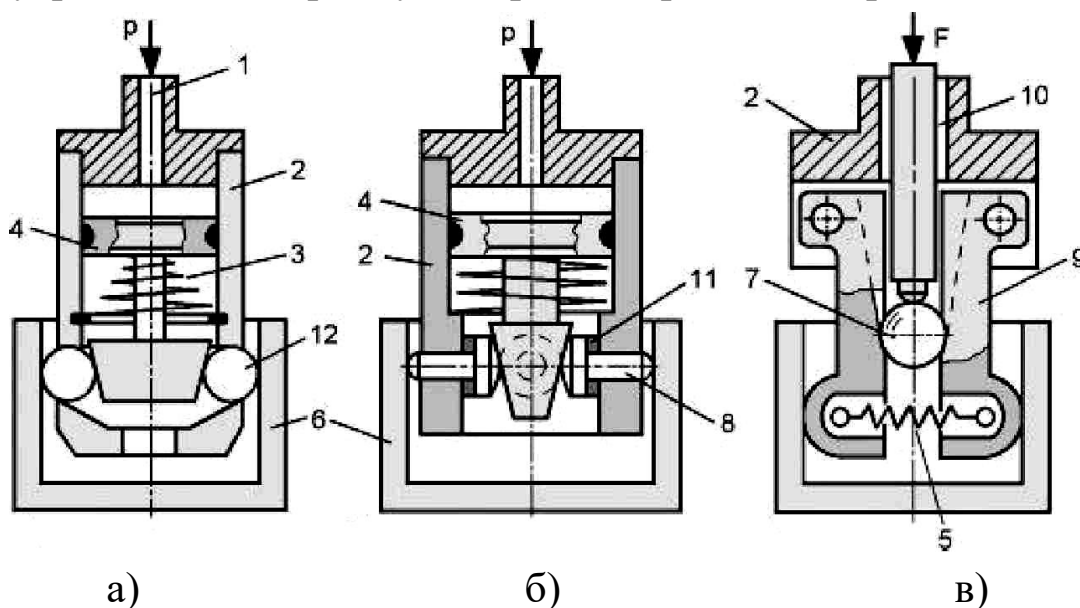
Конструкції ЗП для затиску деталей за внутрішню поверхню:
